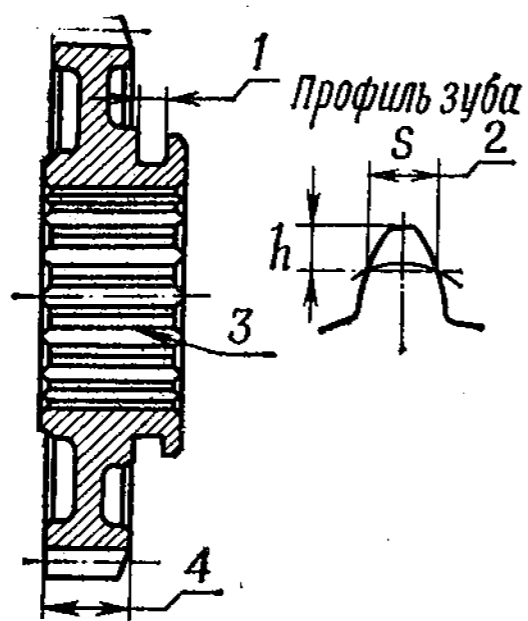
Ведомая шестерня понижающей передачи раздаточной коробки
